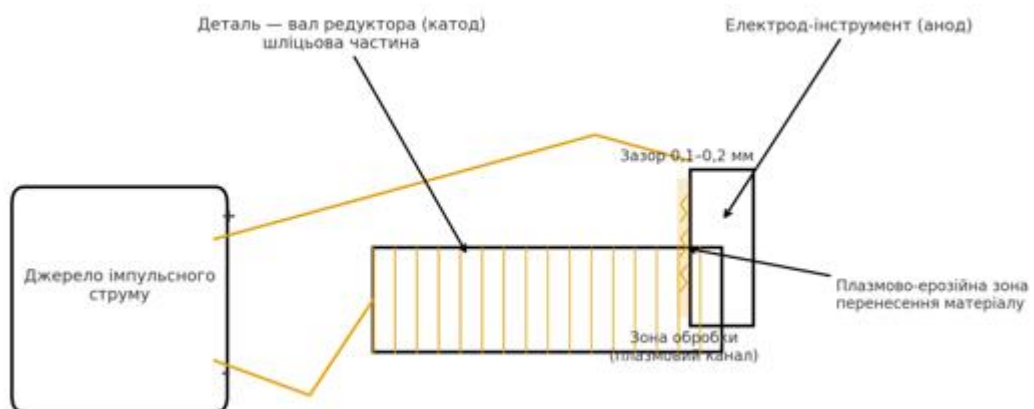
Схема процесу електроерозійної цементації шліцьової частини вала редуктора John Deere 6140 B
